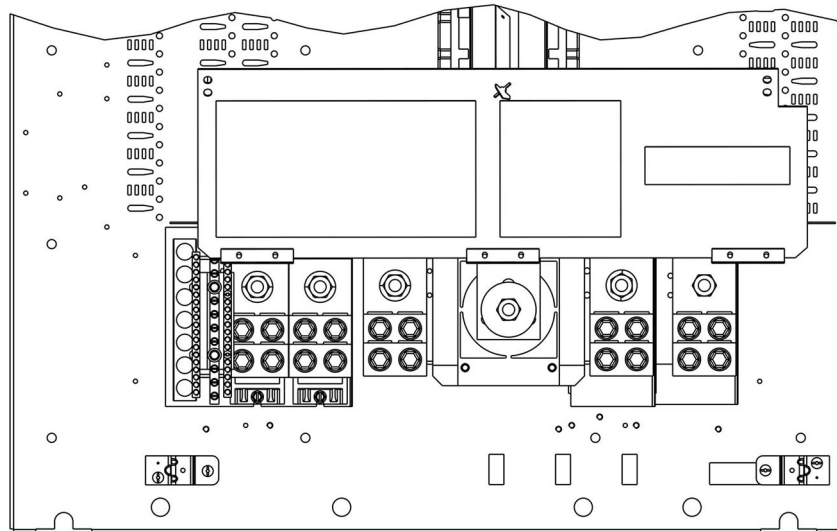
Installation du kit d'assemblage du neutre sur un panneau HCR-U, cosse à serrage illustrée.
